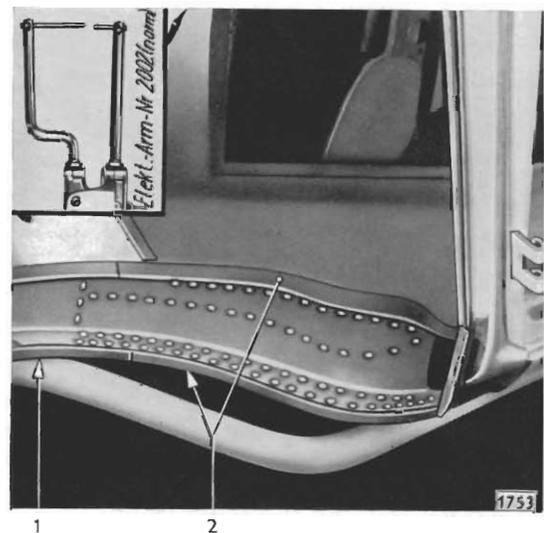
Linken Vorderrahmenlängsträger an Längsträgerrest zangenpunktgeschweißt - rechten Längsträger in gleicher Weise punktschweißen
